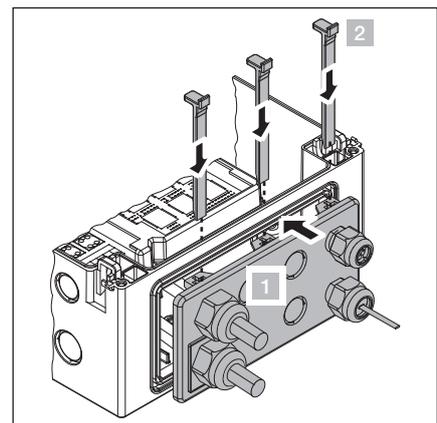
Einbau der Verschraubungsflanschplatte
